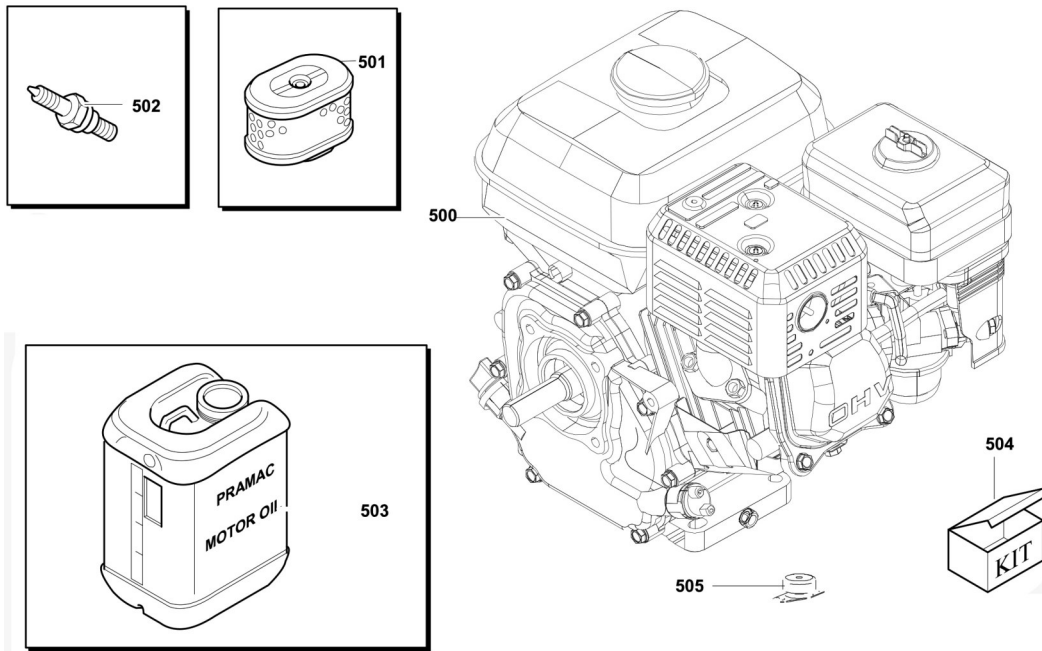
Ersatzteilzeichnung 3 - PG 400 SR
